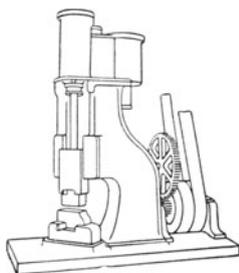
Einständriger Hammer mit Hohlgußständer.
